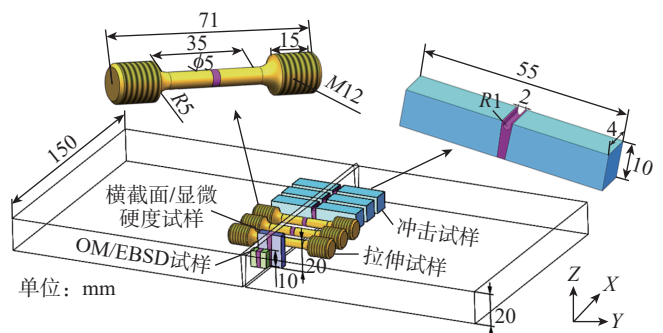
TA15 接头电子束焊接取样位置及尺寸
